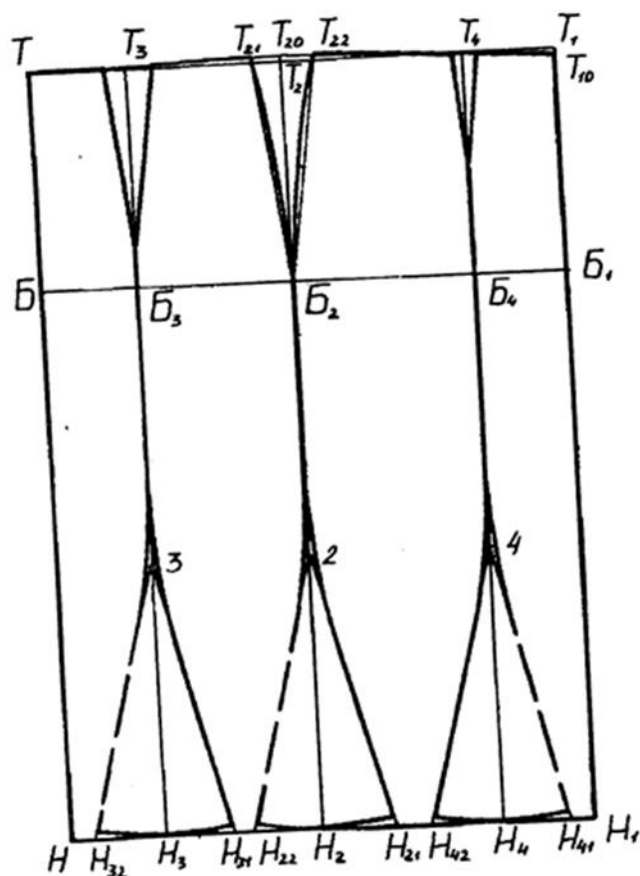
Чертеж конструкции шестиклиньевой юбки с годеобразным расширением к низу
